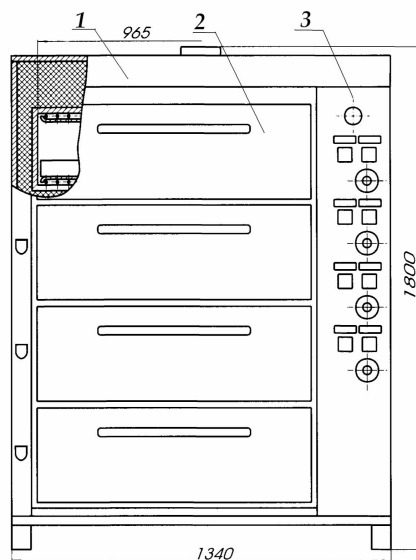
Піч ХПЕ 750: 1 - корпус; 2-дверцята; 3 - пульт керування; 5 – пекарна камера; 6 – форми.
